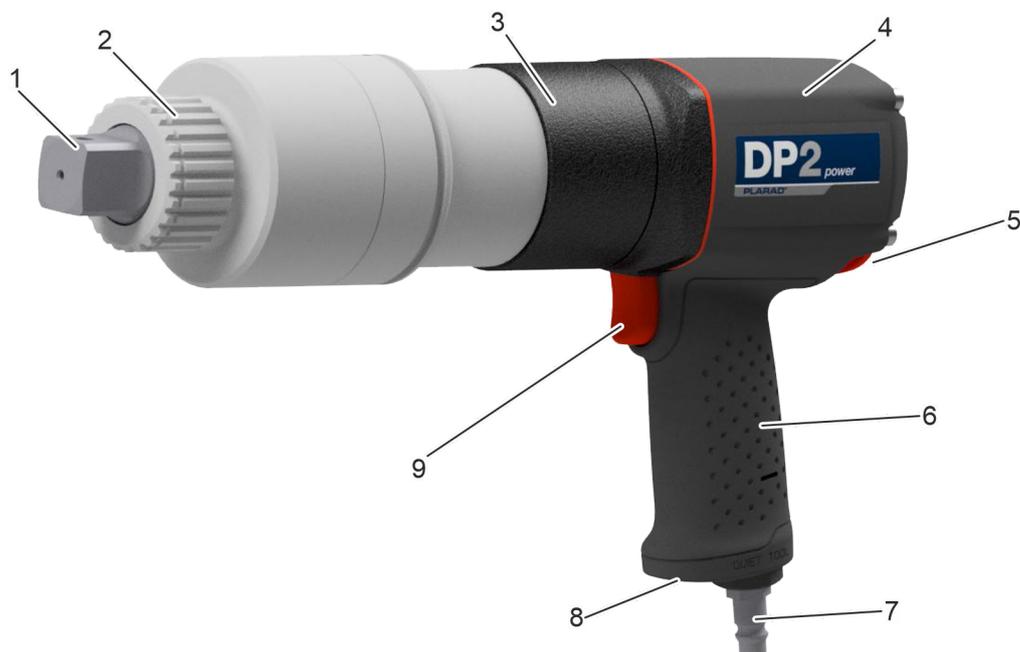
Vue d'ensemble de la visseuse DP2power
